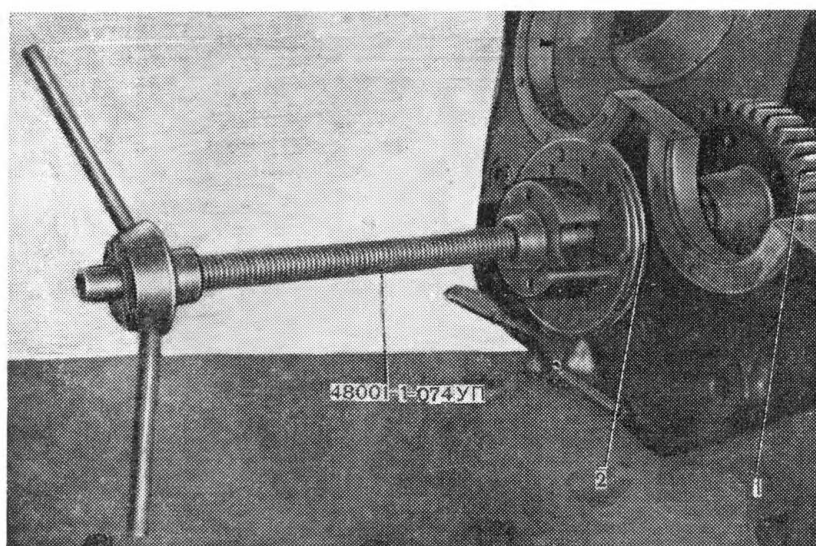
Выпрессовка обоймы шариковых и роликовых подшипников:
